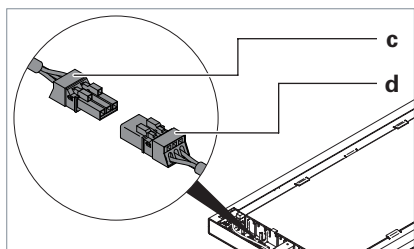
Collegamento della testa dell'apparecchio d'illuminazione, parte 2.
